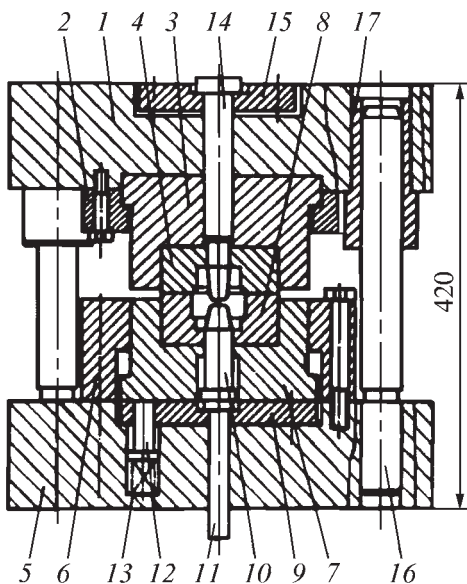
Штамповый блок с «плавающей» матрицей для штамповки в закрытых штампах с разъемными матрицами
